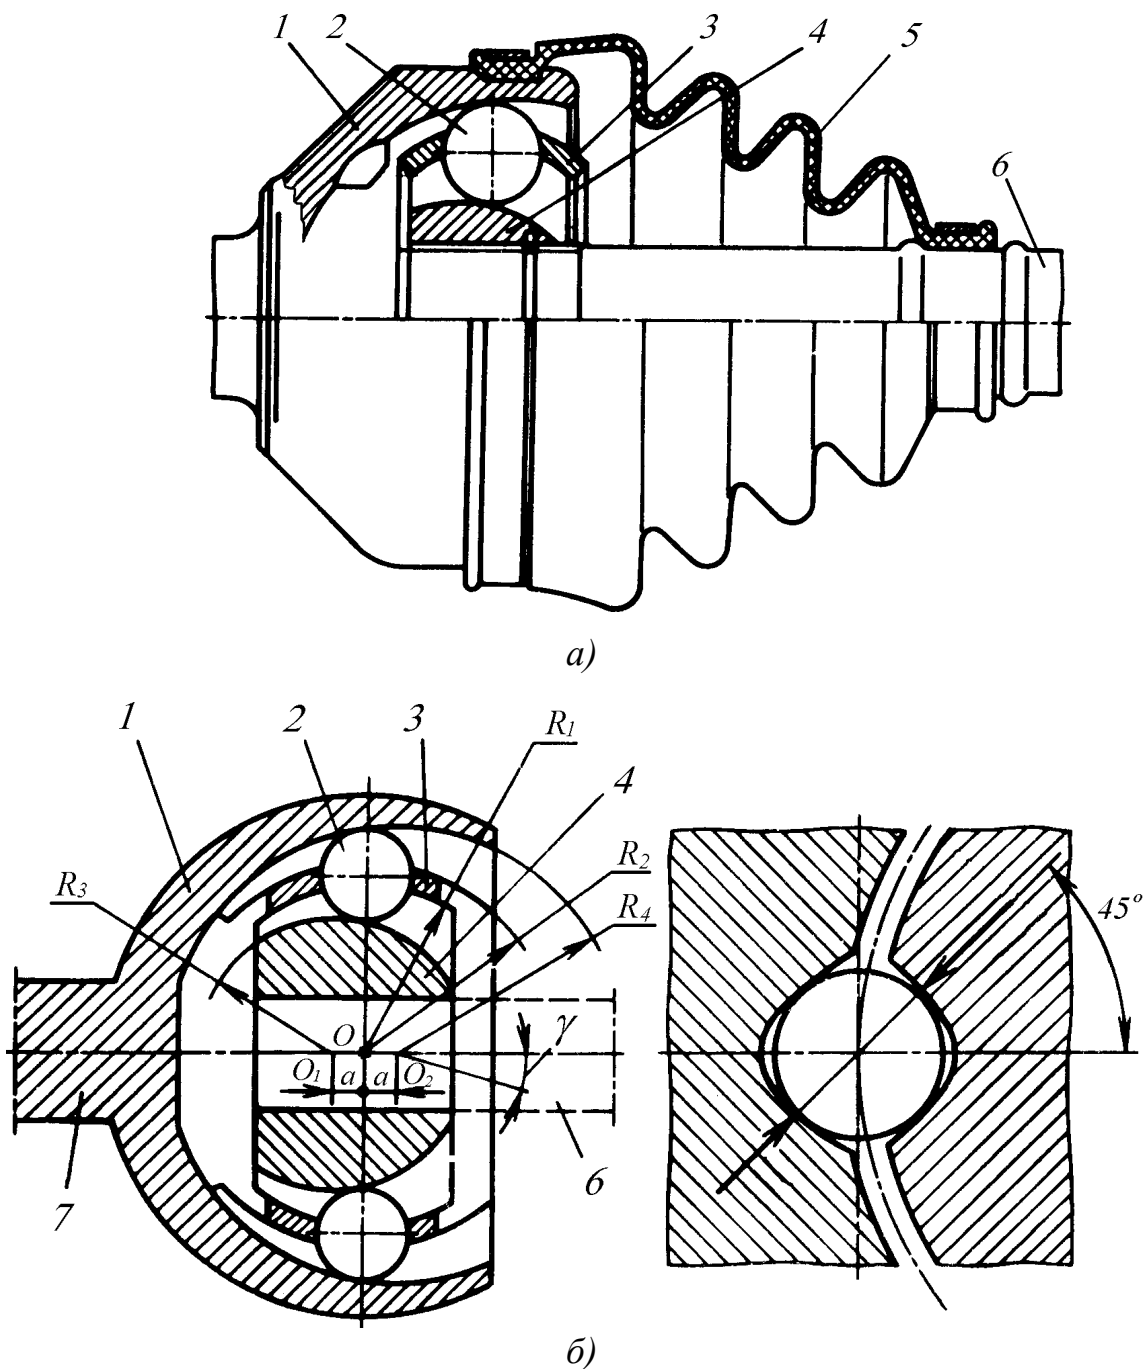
Шестишариковый карданный шарнир типа “Бирфильд”:
